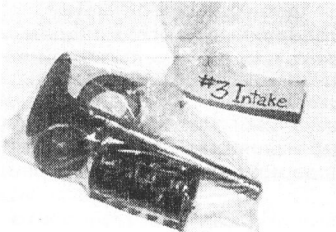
Перед разборкой головки цилиндров подготовить помеченные полиэтиленовые мешки (по одному на каждый клапан), по которым можно разложить все детали клапанного механизма, относящиеся к конкретным клапанам.
